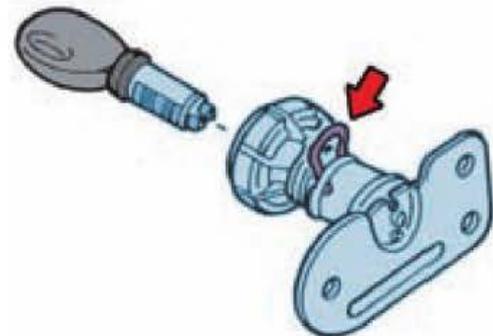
Extracción del bombín del conjunto de la cerradura.
